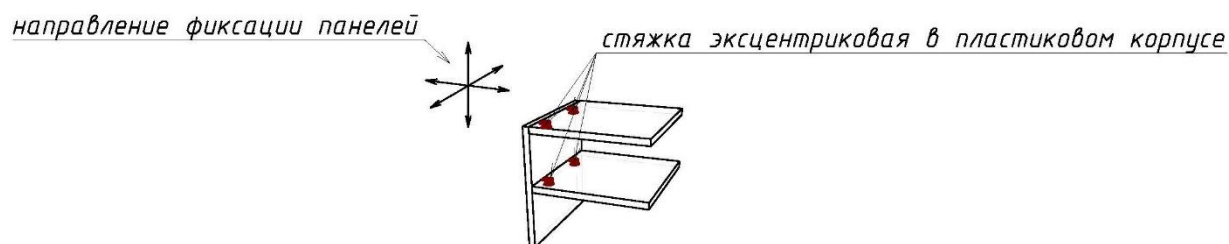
Применение эксцентровой стяжки в пластиковом корпусе (БМ)
